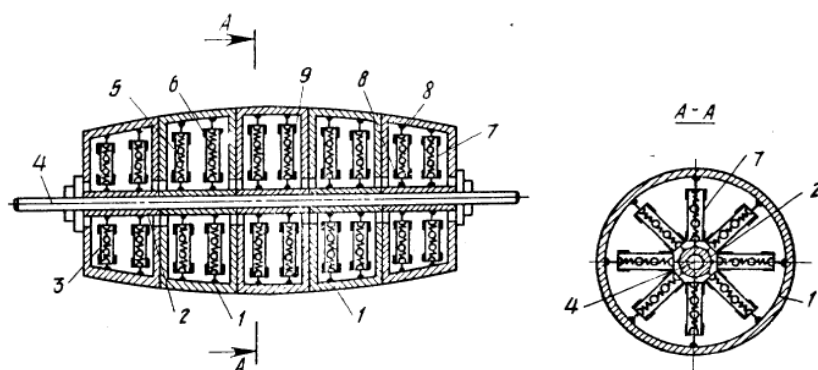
Виброударные каток для обработки почвы (А.с. 1380624)
